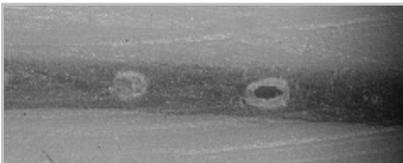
Поры в сварном соединении образца из PEEK
